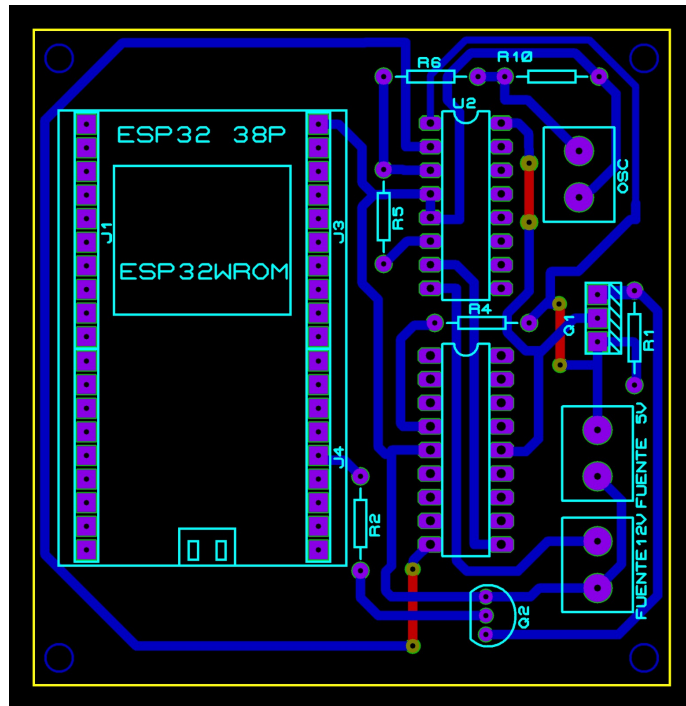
Esquemático de la placa PCB en 2D. Autor propio.
